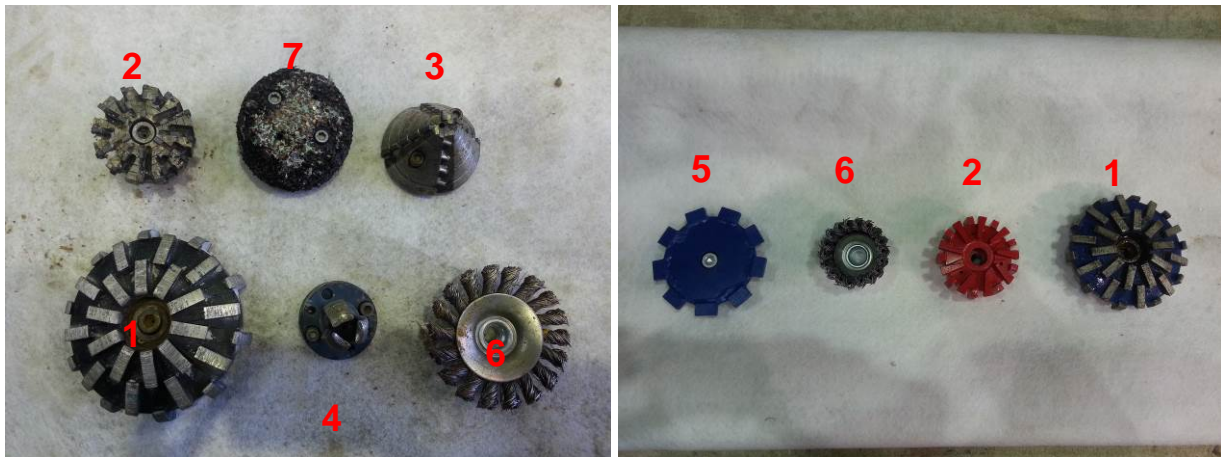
Fräskopf-Equipment, Beispiele für eingesetzte Fräs- und Bürstenköpfe: Pilzkopffräser (1), Einlaufnäser (2), Kegelfräser (3), Nutenfräser (4), Scheiben-/Tellerfräser (5), Scheiben-/Topfbürste (6) und Schleifscheibe (7)
